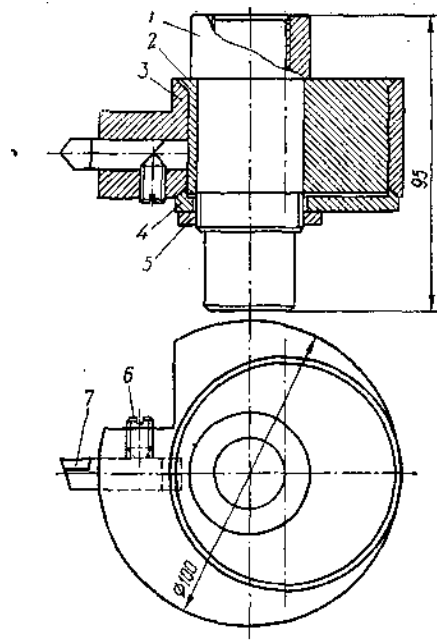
Різцева оправка для обробки поверхонь отворів корпусів коробки передач:
